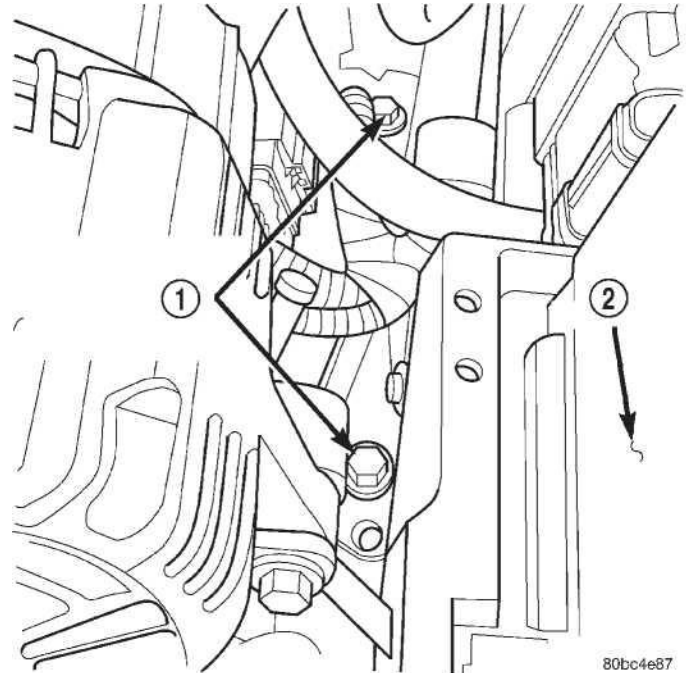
Болты пластины подоконника опоры двигателя - Leftside
